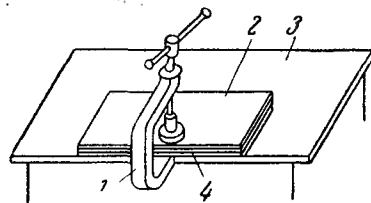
Приспособление для измерения толщины лаковой пленки. 1 — трубка для сжатия пакета листов; 2 — листы стали; 3 — стол; 4 — измеряемая величина.
